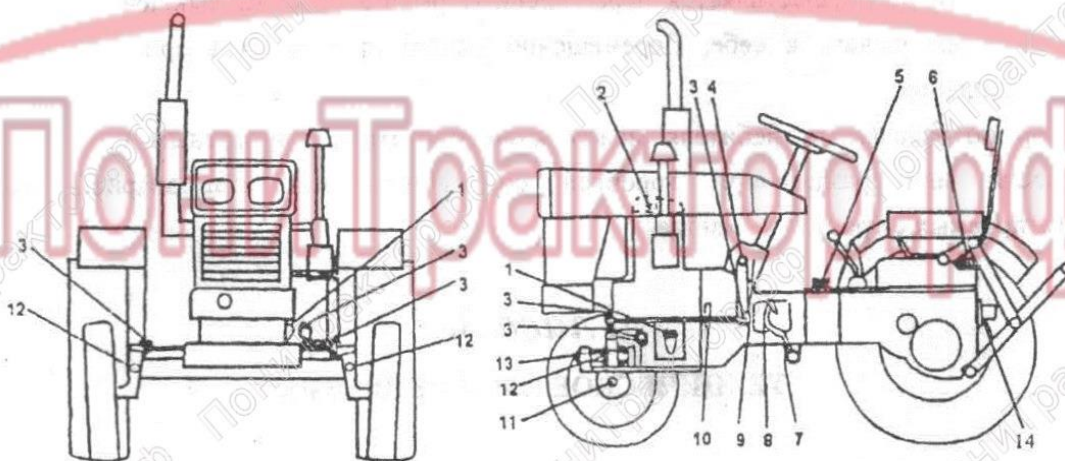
Карта смазки трактора: 1-картер двигателя; 2-коромысло; 3-шаровой палец поворотной тяги; 4-эксцентриковая втулка механизма рулевого управления; 5-коробка передач; 6-подъемник; 7-втулка валика педали муфты сцепления; 8-выжимный подшипник; 9-механизм рулевого управления; 10-передний подшипник муфты сцепления; 11-подшипники передних колес; 12-втулка качания
